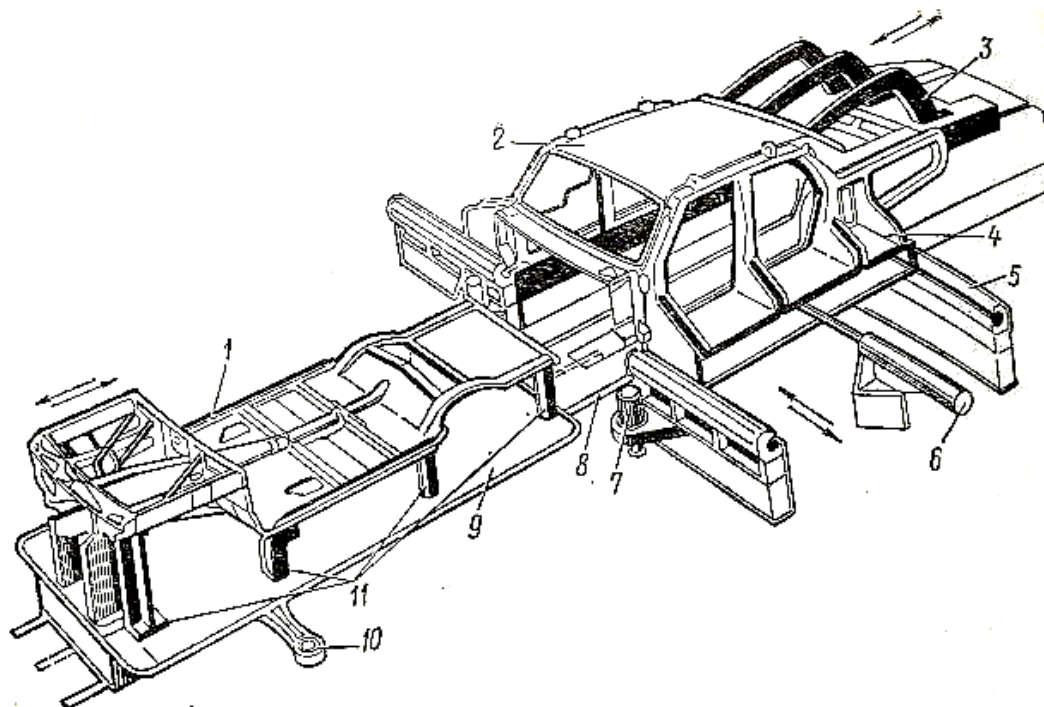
Схема сборки кузова ГАЗ-24 в главном кондукторе:
